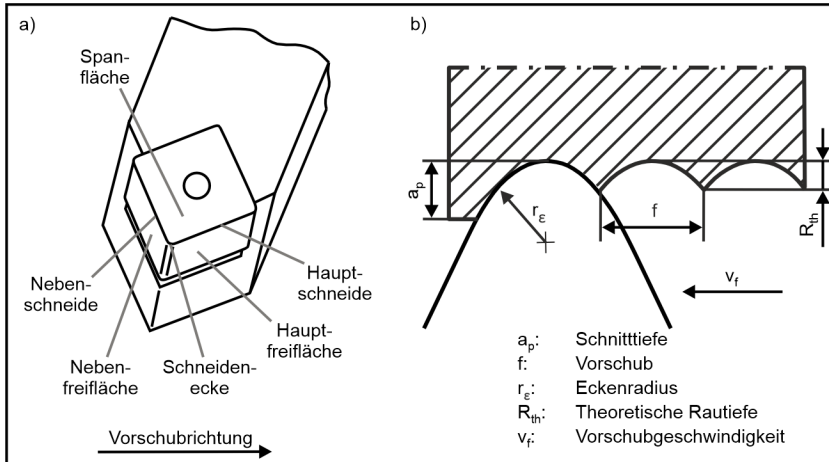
a) Aufbau eines Werkzeughalters;
